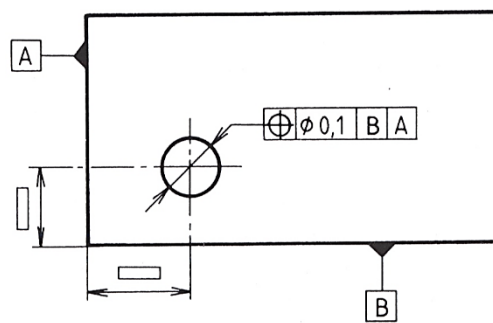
Značení soustavy základen a jejich pořadí[8]
